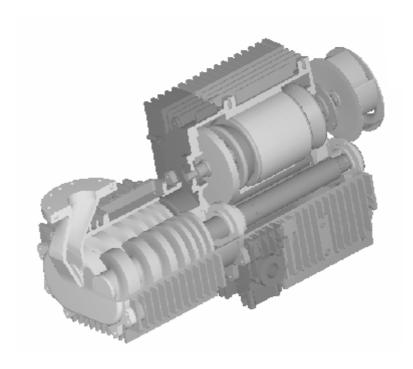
Innerer Aufbau der Schraubenvakuumpumpe SP630 mit fliegend gelagerten Rotoren, integriertem Motor und Luftkühlung. Durch das Getriebe laufen die Rotorwellen mit der doppelten Drehzahl der Motorwelle. Die Motorwelle trägt an ihren zwei Enden Ölpumpe (vorne) und Lüfter (hinten).
